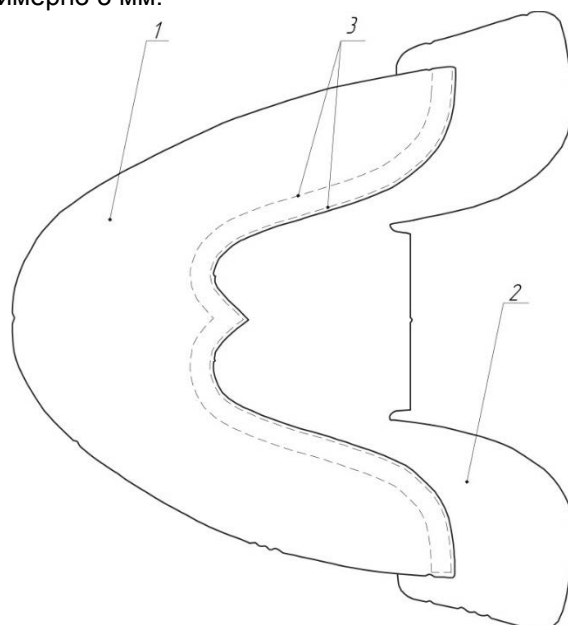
Заготовка верха обуви: 1 – носок; 2 – союзка; 3 – соединительные строчки
